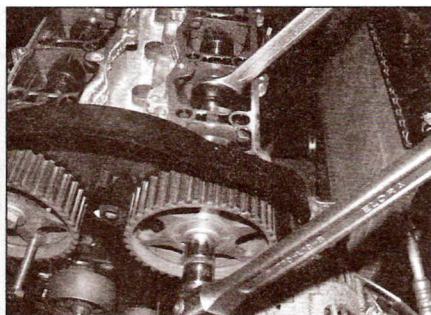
Используйте рожковый гаечный ключ для придерживания распределительного вала при отпускании болта крепления зубчатого шкива (двигатели 1.6 л)
